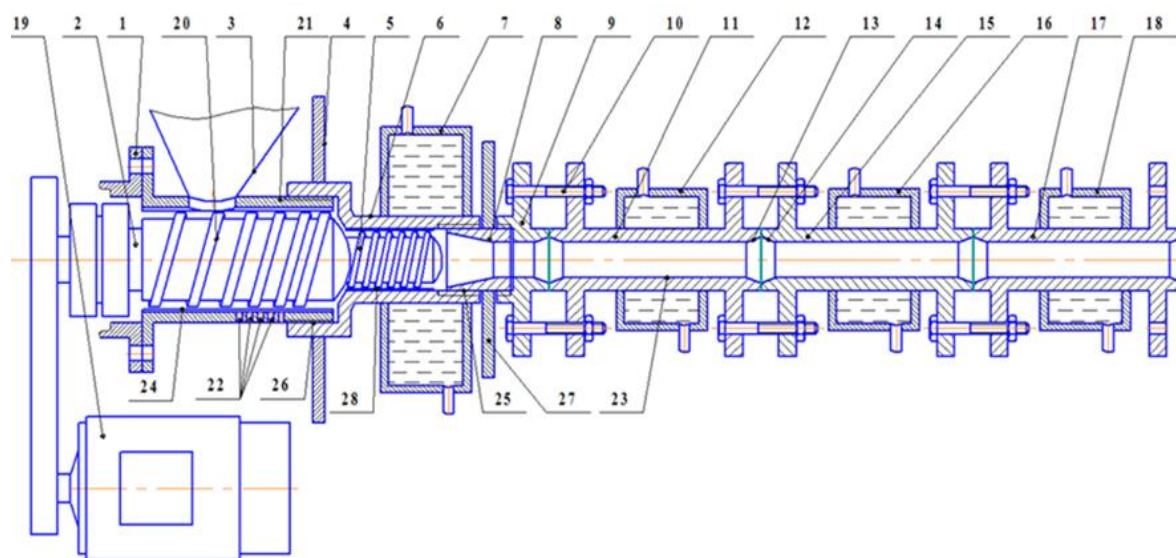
Схема шнекового розробленого прес-екструдера для виготовлення паливних брикетів з пристроєм остаточного формування:
